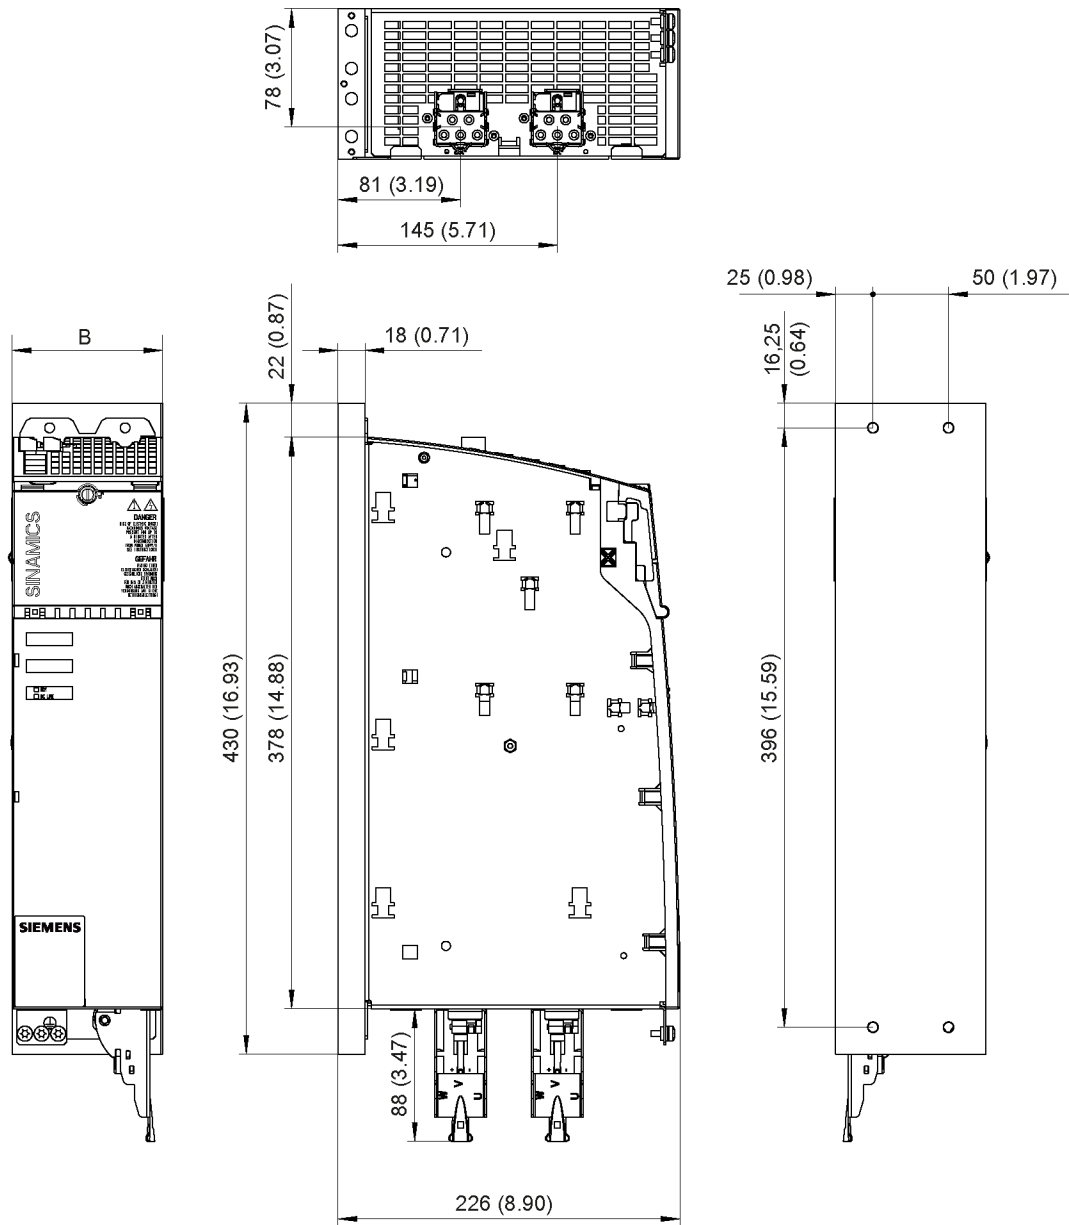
Croquis acotado de Motor Modules Booksize de 30 A y 2 x 18 A con Cold Plate, todas las medidas en mm y (pulgadas)
